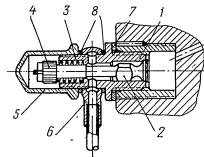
Пусковой клапан (разрез). 1—корпус, 2—клапан, 3—пружинка, 4—гайка, 5—кольцо, 6—поворотный штуцер, 7—прокладка, 8—пробка.
